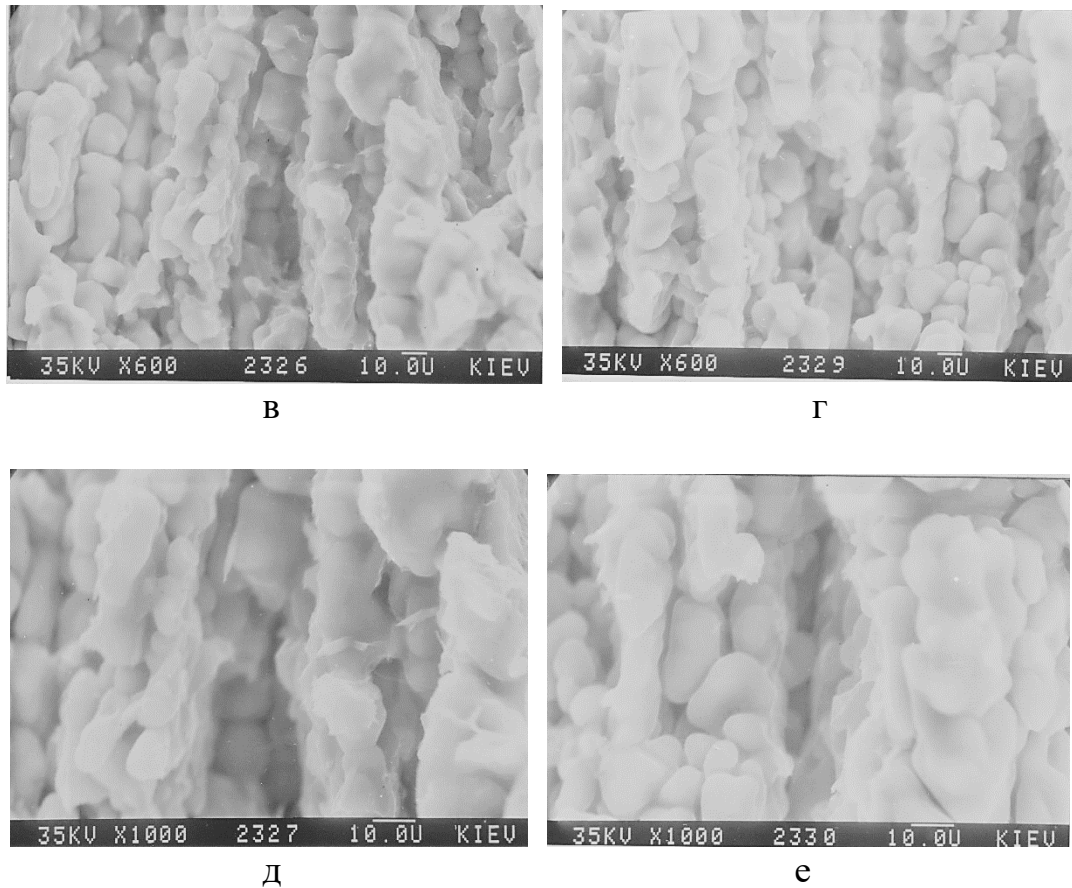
Фрактограммы поверхности излома по горячей трещине, образованной в зоне сплавления со стороны сплава 1565чМ при повторном проплавлении технологической пробы в виде узкой пластины критических размеров, вырезанной из стыкового сварного соединения разноименных сплавов 1565чМ и АМг3:
